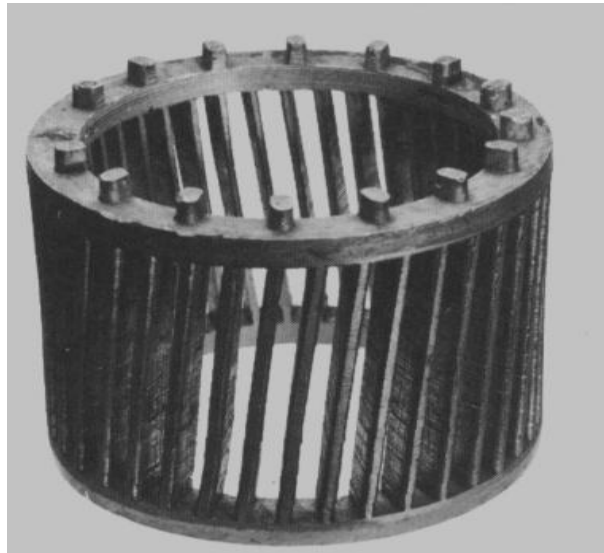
Photo d'un rotor à cage d'écureuil
